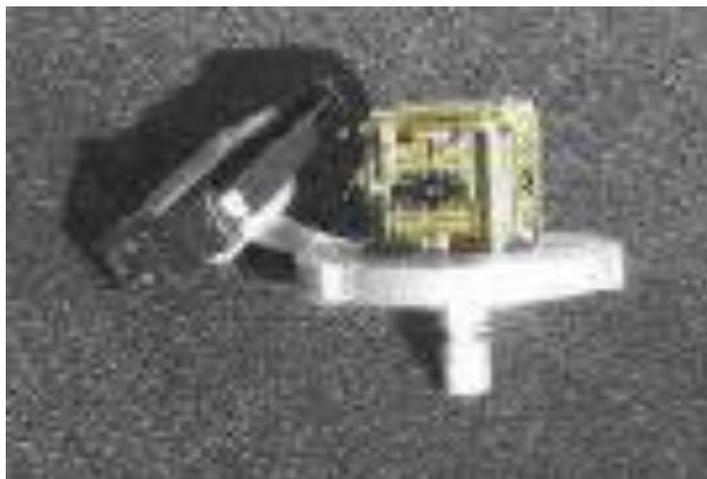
Внешний вид кабельной перемычки в конструкции трехпараметрового датчика
